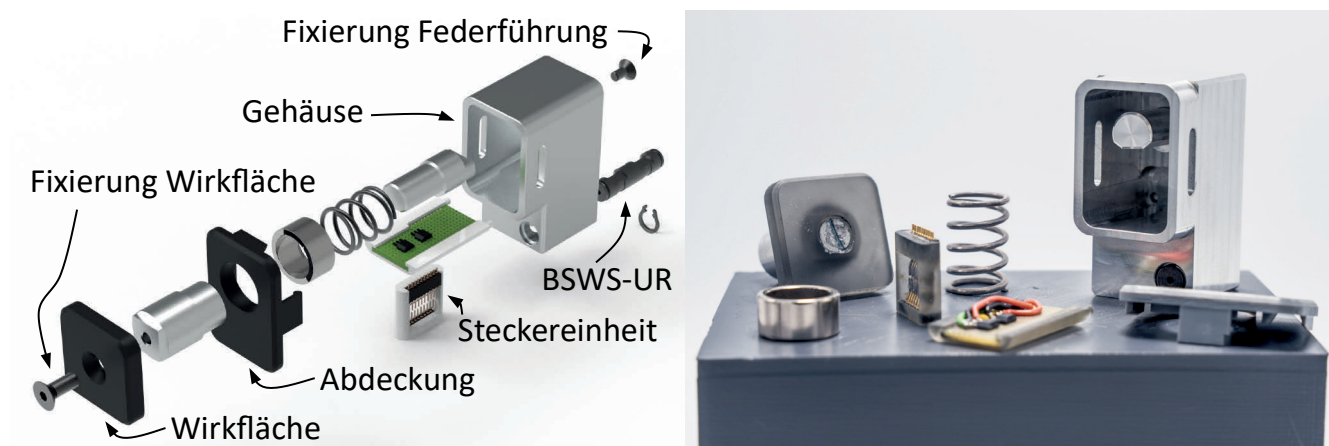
Explosionsansicht der Fingerspitze mit Kraftsensorik
